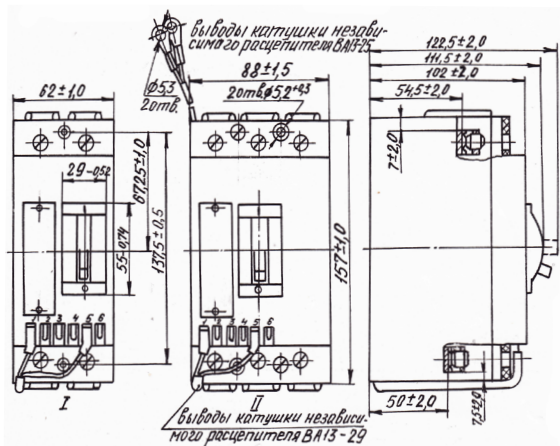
Сверление отверстий под винты крепления двухполюсного и трехполюсного выключателей
